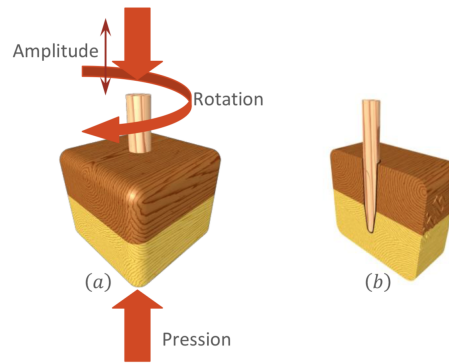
Principe du soudage par friction rotative [46]
